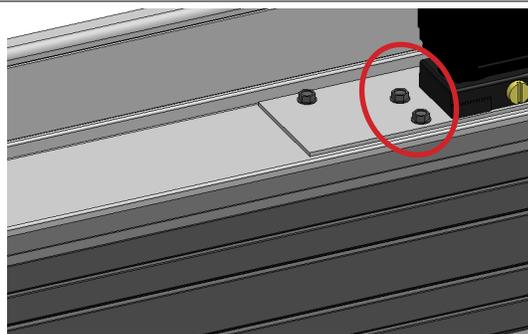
Vuelva a colocar los tornillos de la placa de transporte de la puerta.
